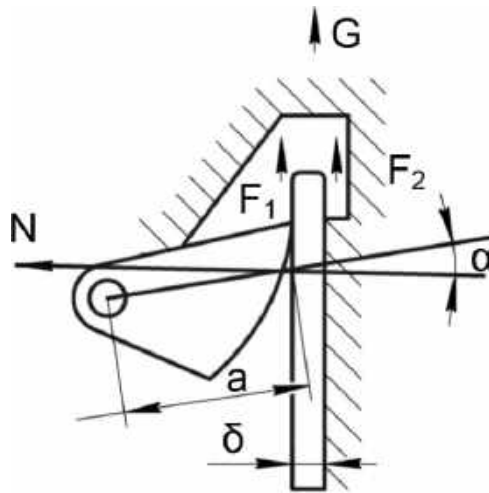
Розрахункова схема клинового захоплювача
